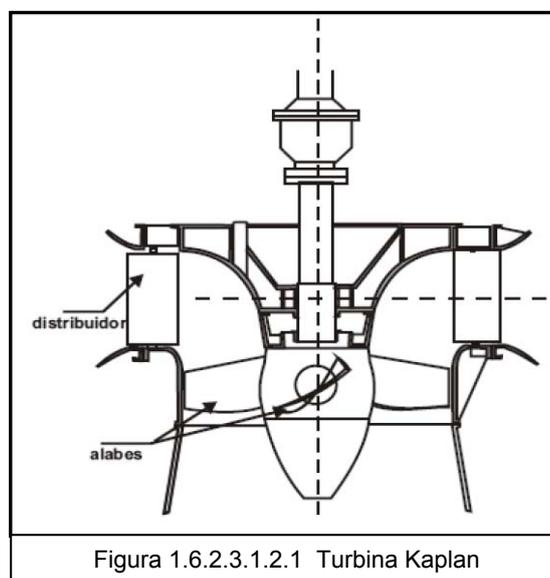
Turbina Kaplan
